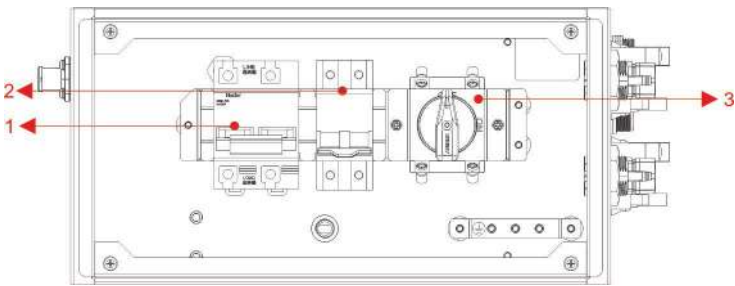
Parte de la caja de conexiones sin la tapa-Vista frontal
